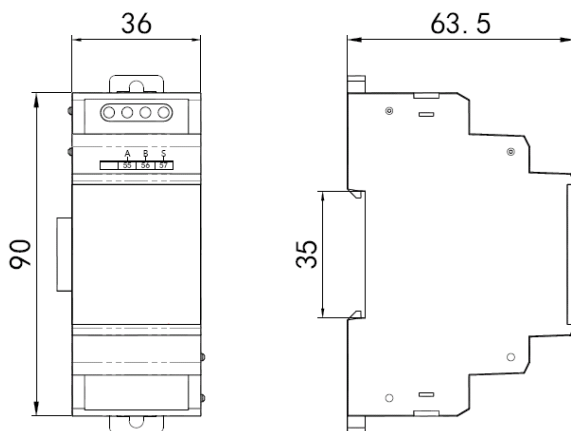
Внешний вид и габаритные размеры модуля связи C10
